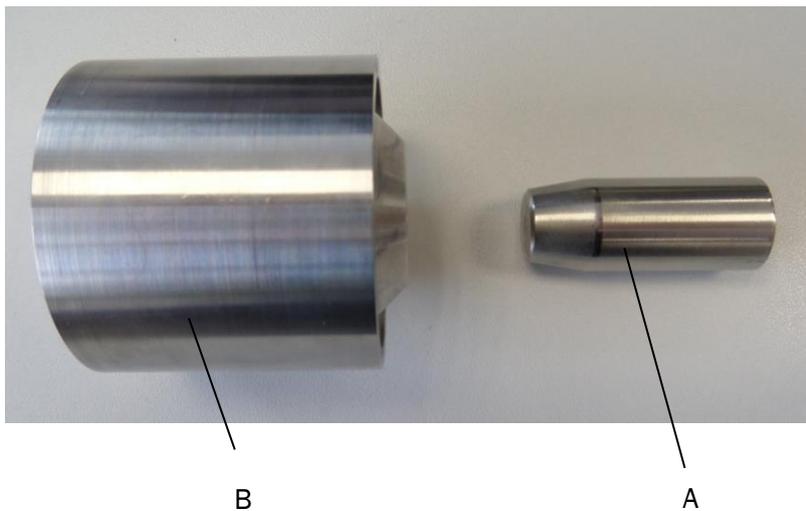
Montagehilfswerkzeug Montagekonus (A) und Montageamboss (B)
